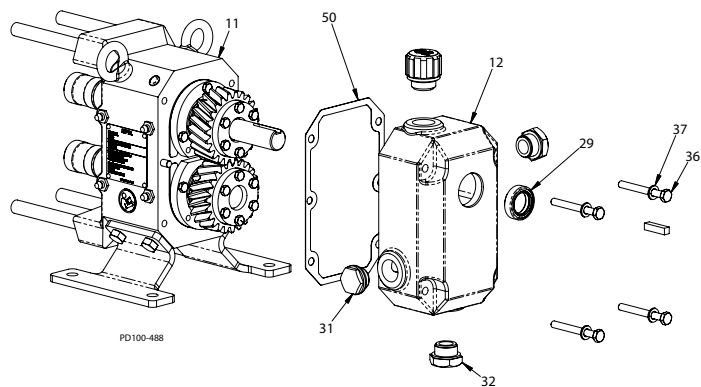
Retirez le couvercle de la boîte d'engrenages
